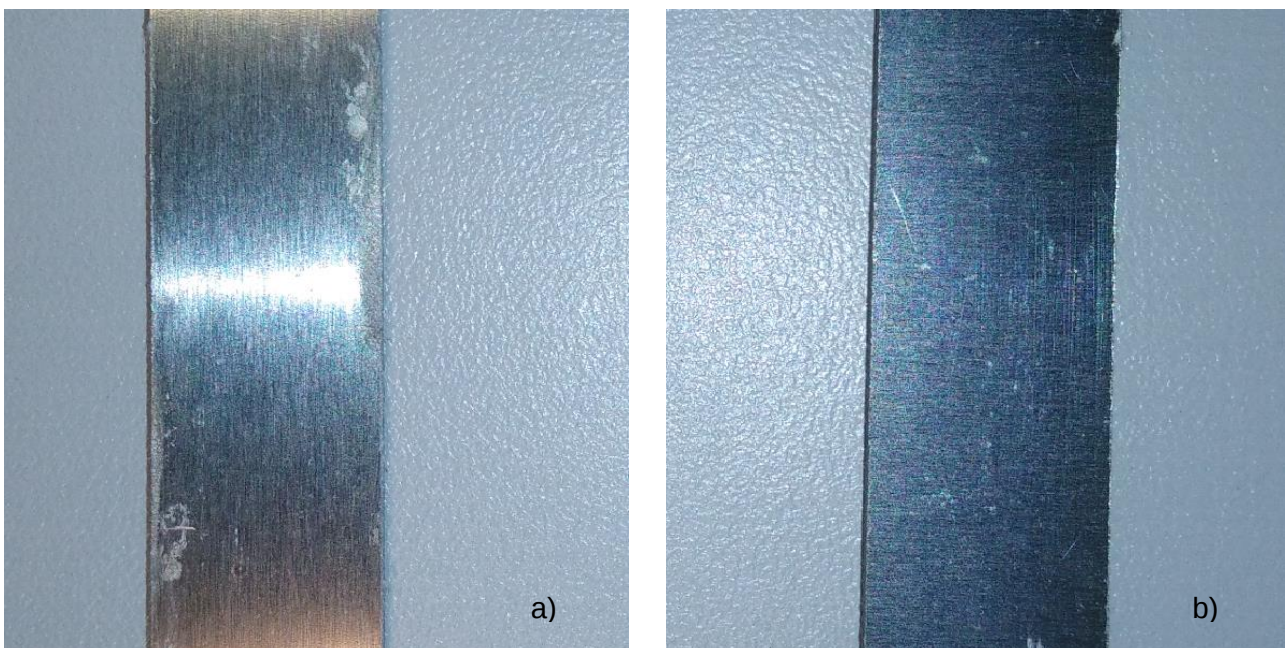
Dirección de laminado longitudinal (a) y transversal (b)
